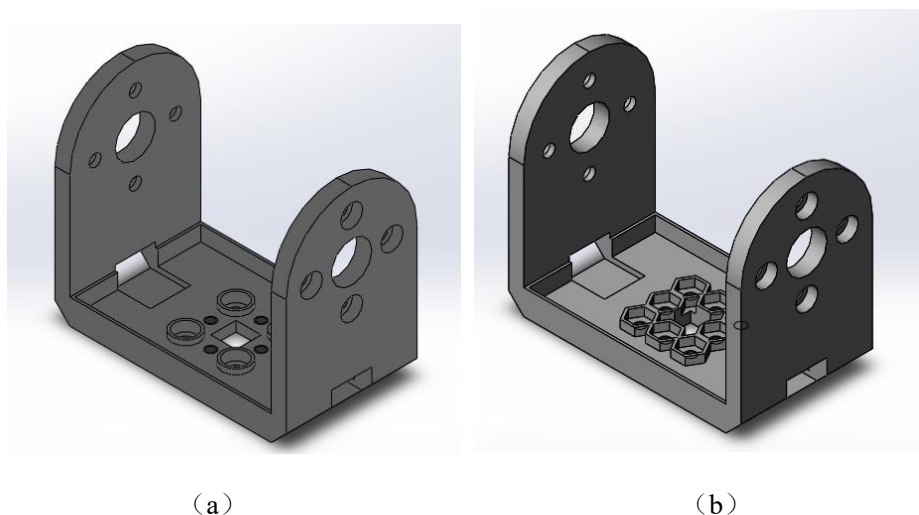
关节 1 零件图 (a) 有装螺丝的结构 (b) 有装螺母的结构
